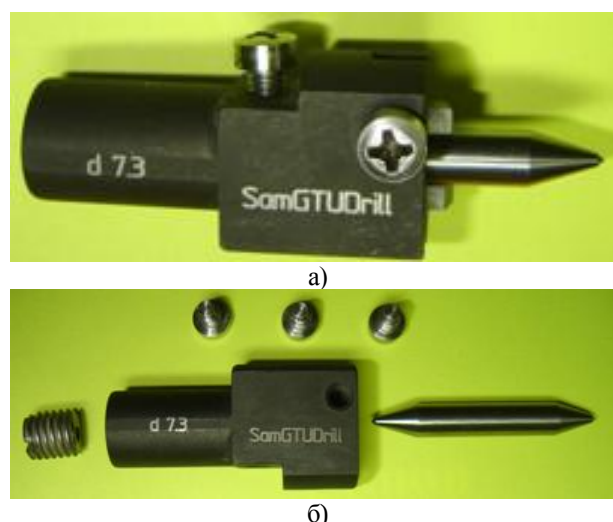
Общий вид перфороватора со сменной твердосплавной вставкой для обработки стальных заготовок (а) и вид перфороватора в разборе (б)
